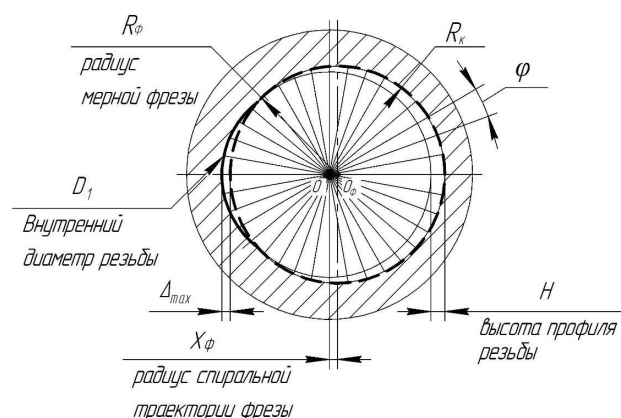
Схематический профиль резьбы в поперечном сечении детали
